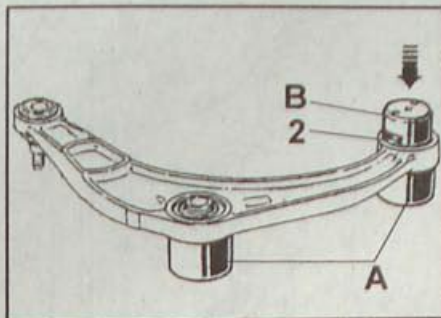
Выпрессовка заднего сайлент-блока из нижнего рычага : А – кольца приспособления Т.АВ. 1274; В – втулка приспособления Т.АВ. 1274-01; 2 – расположение заднего сайлент-блока
